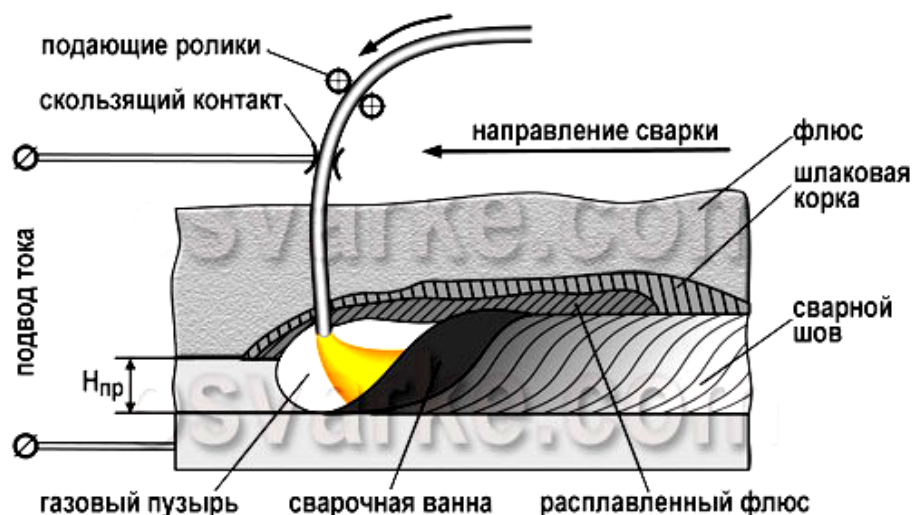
Схема дуговой сварки под флюсом
